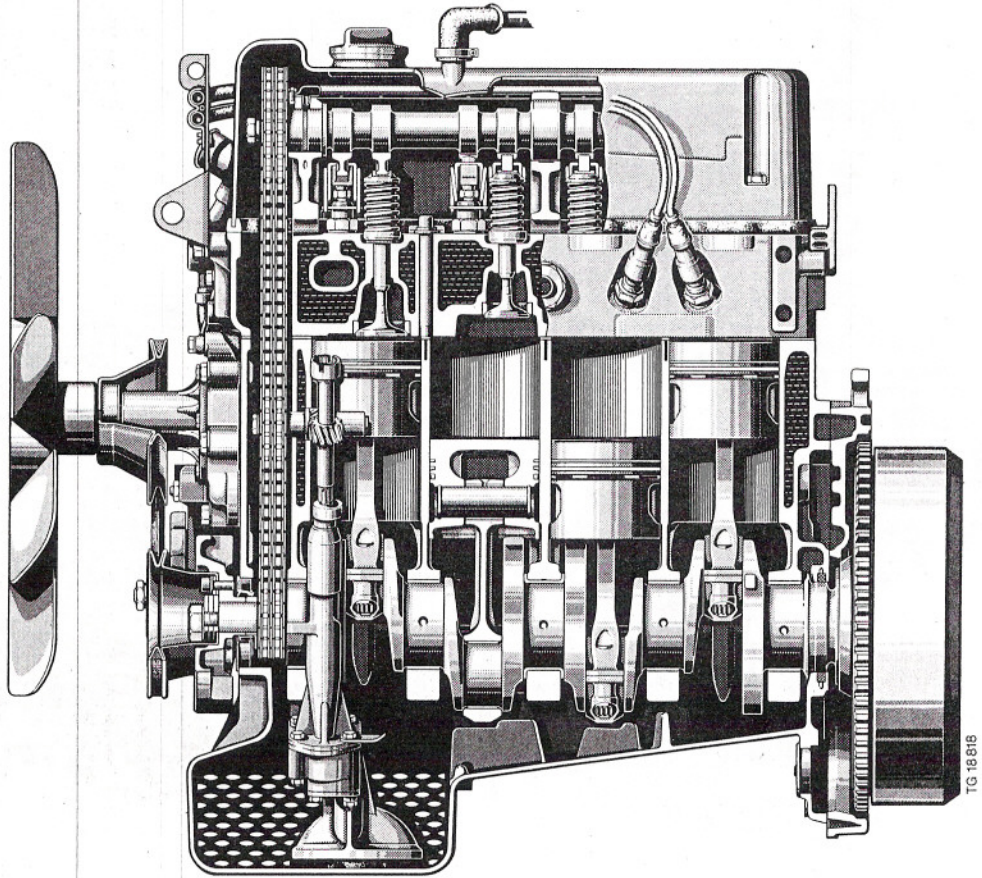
Motor de gasolina 115 (Ejec. 115.973)
